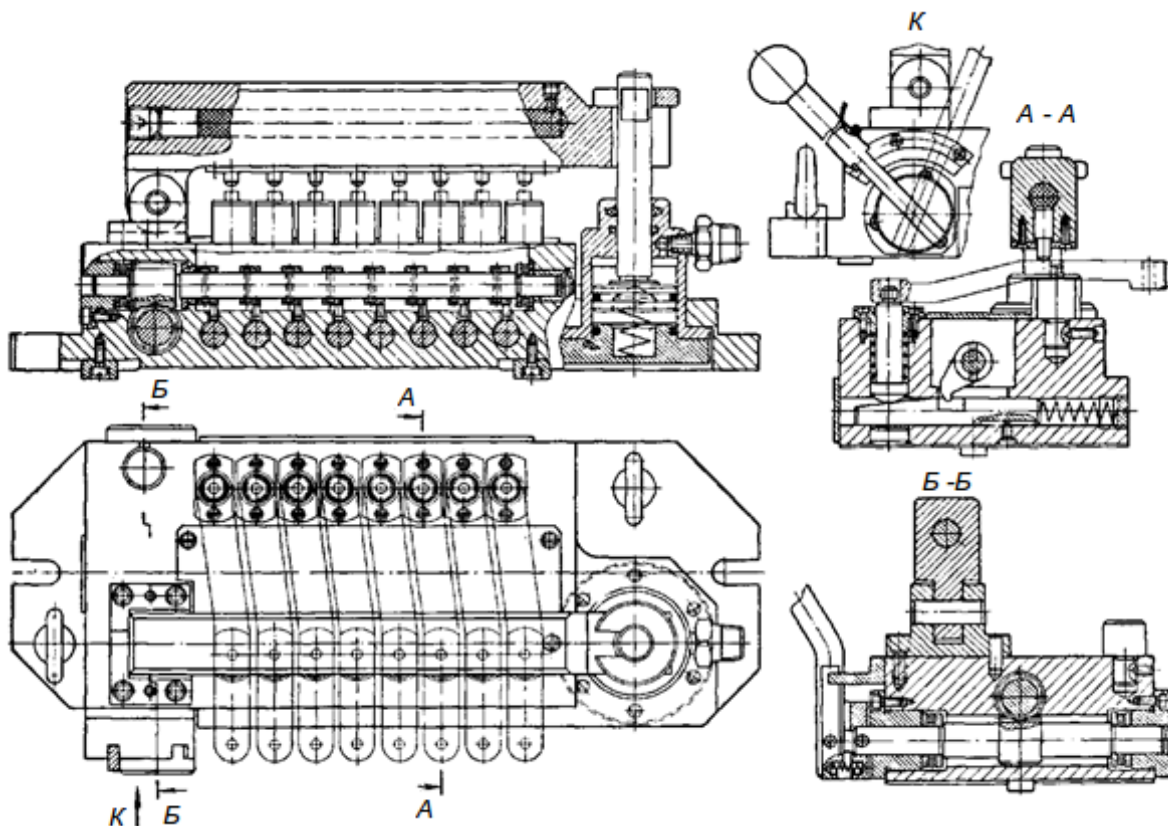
Схема пристосування для базування і закріплення важеля та координування фрези при фрезеруванні торця бобишки важеля
